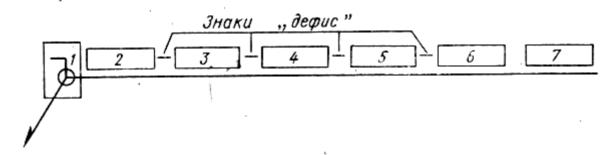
Структура условного обозначения шва сварного соединения:
